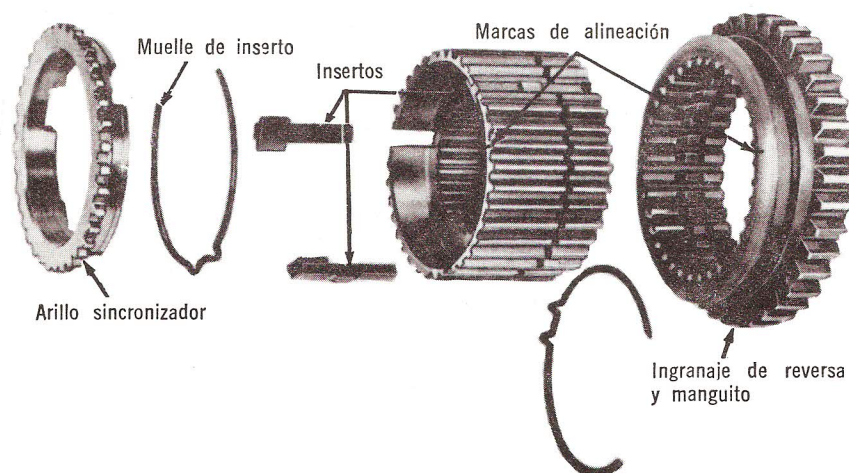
Componentes de Sincronizador de 1ª y Reversa.
